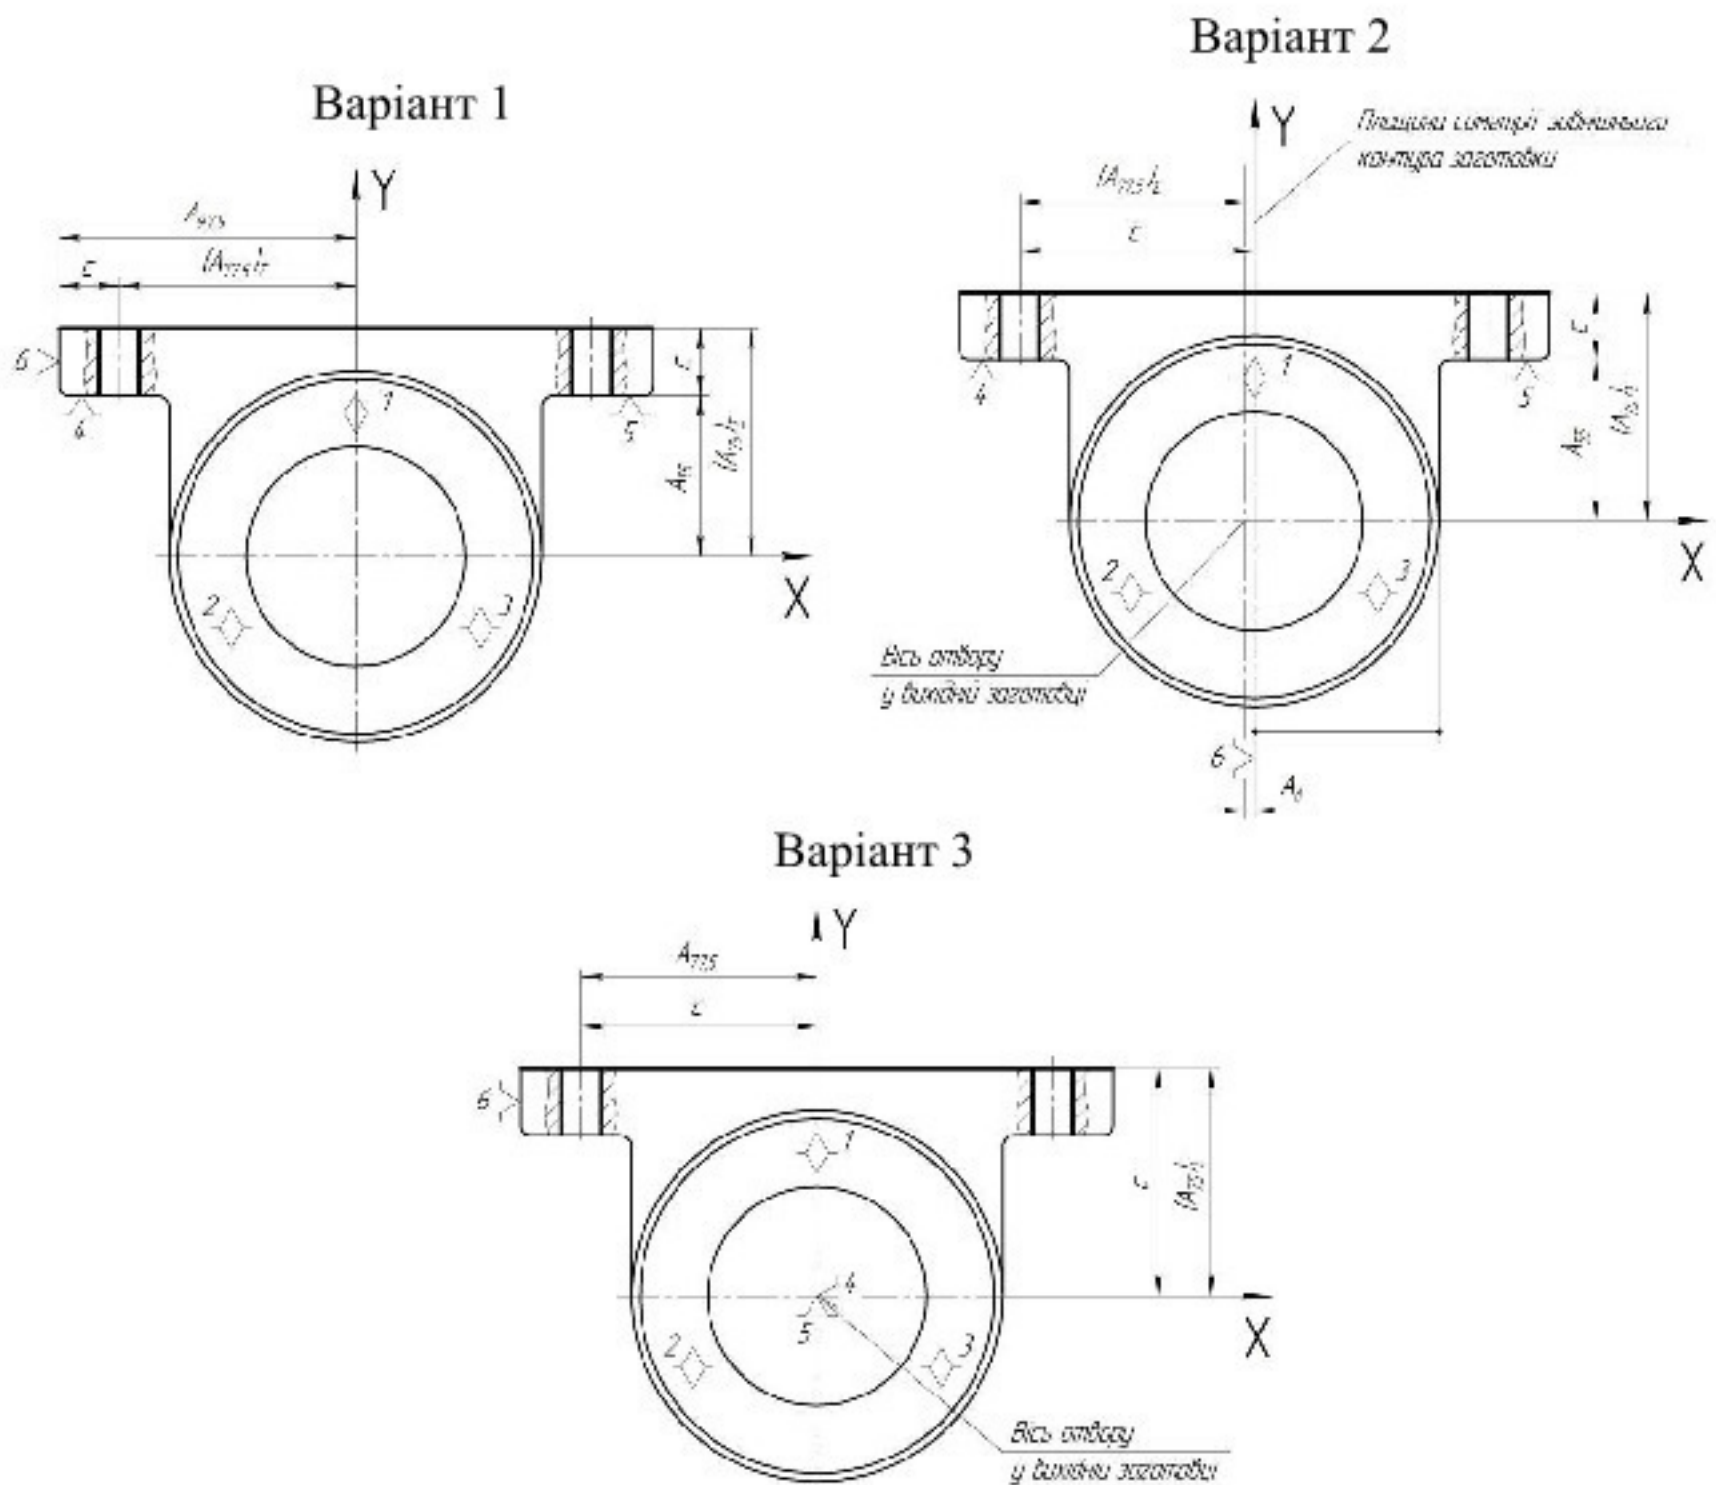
Варіанти схеми базування заготовки деталі типу «Корпус підшипника 420.008-01» на першій операції механічної обробки з технологічними розмірними ланцюгами для визначення похибки базування
